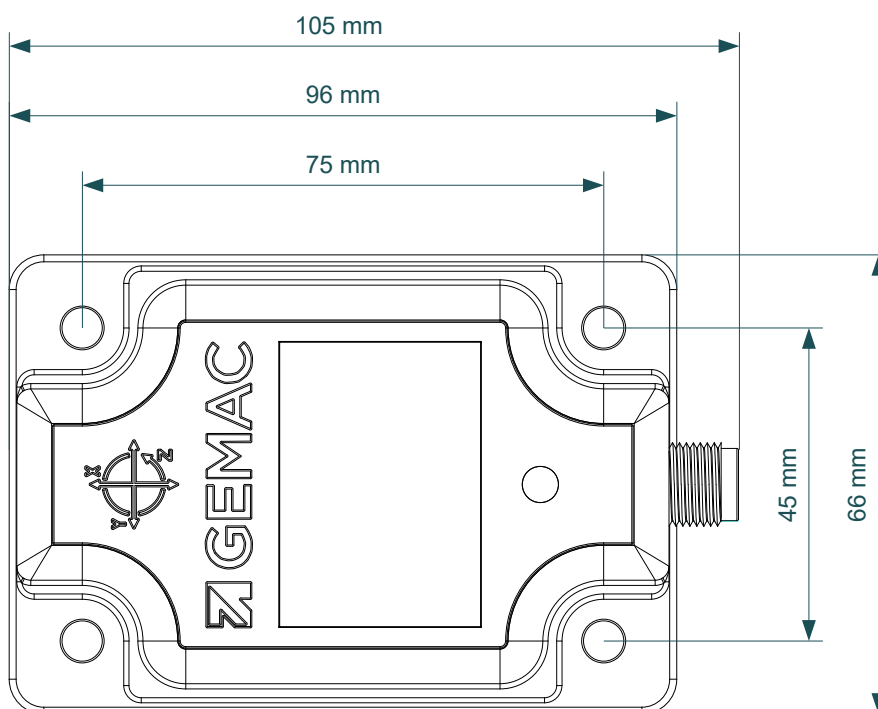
Befestigungsbohrungen (Maße in mm)
